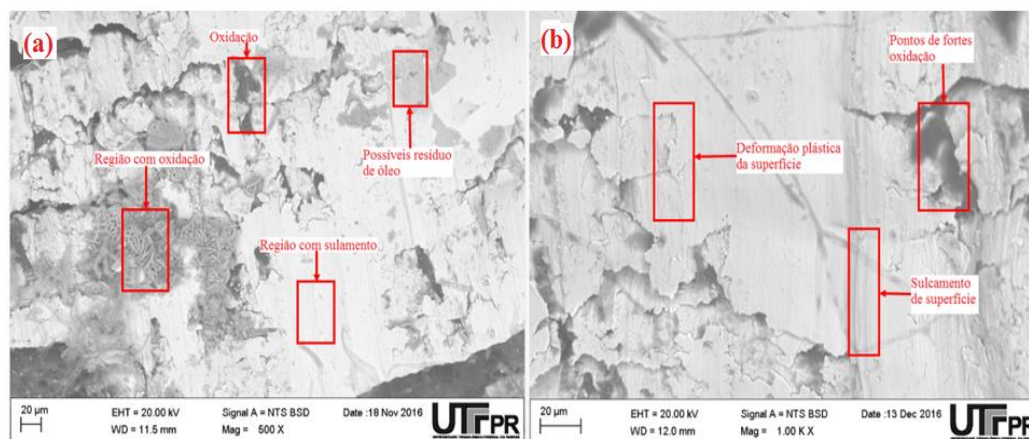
Imagens em MEV: (a) cavaco usinado com fluido de corte utilizando Pinhão manso; (b) cavaco usinado com fluido de corte utilizando Tungue.
